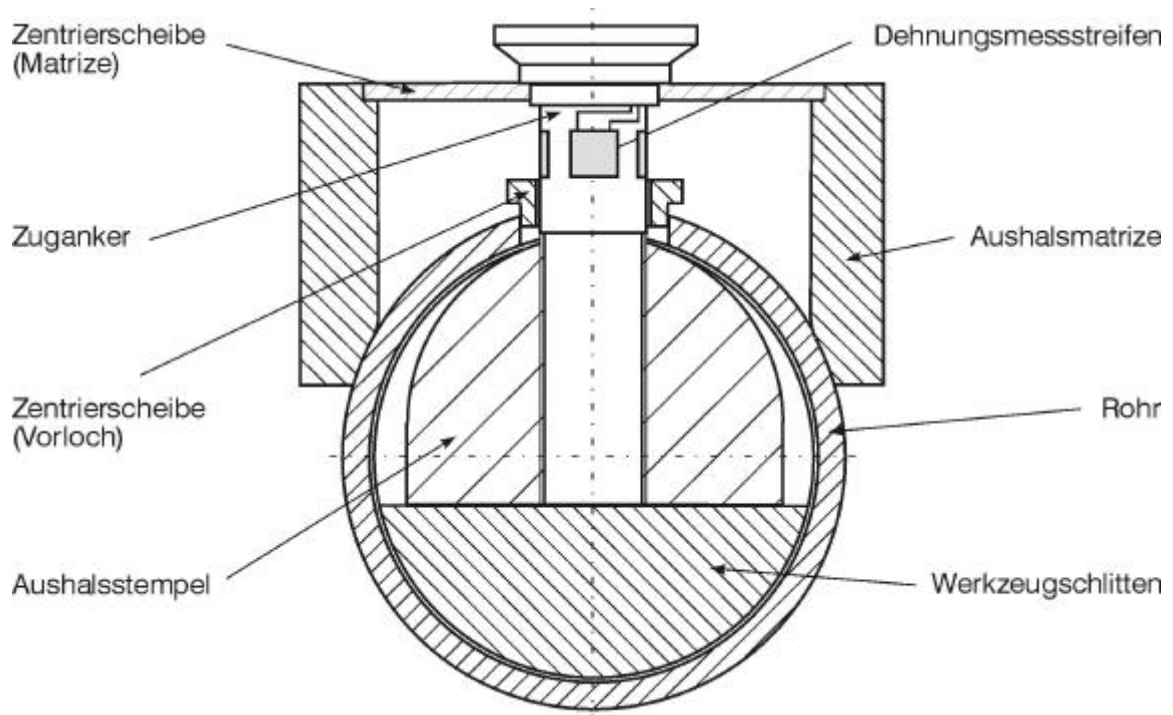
Aufbau des Rohraushalswerkzeuges
